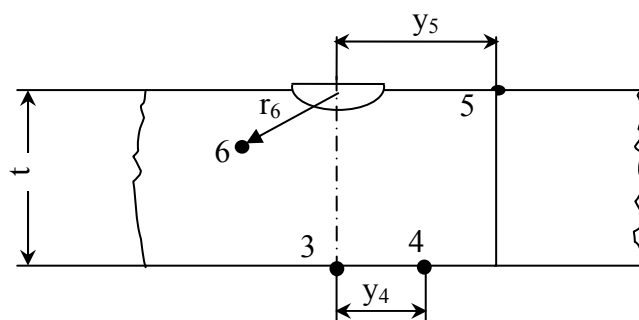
Схема дуговой наплавки валика на пластину вдали от кромок
